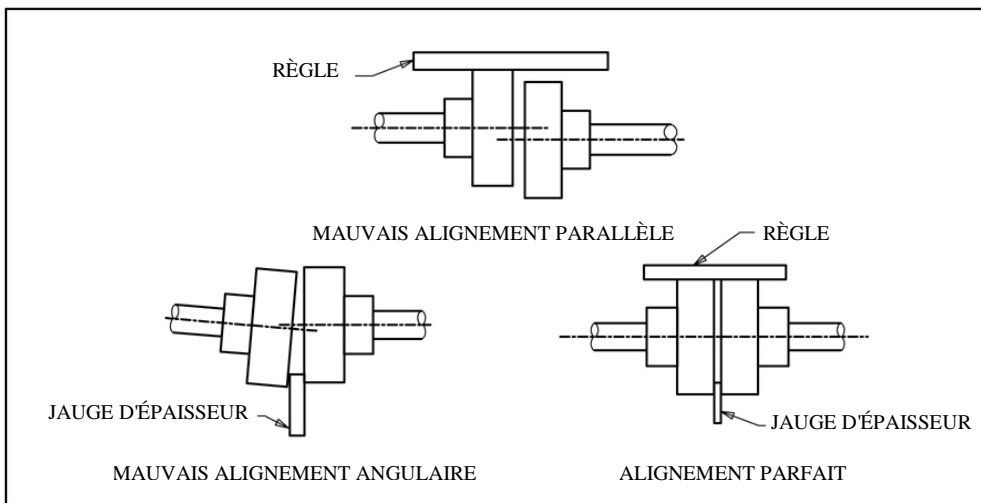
TESTER L'ALIGNEMENT, RÉGLETTE
